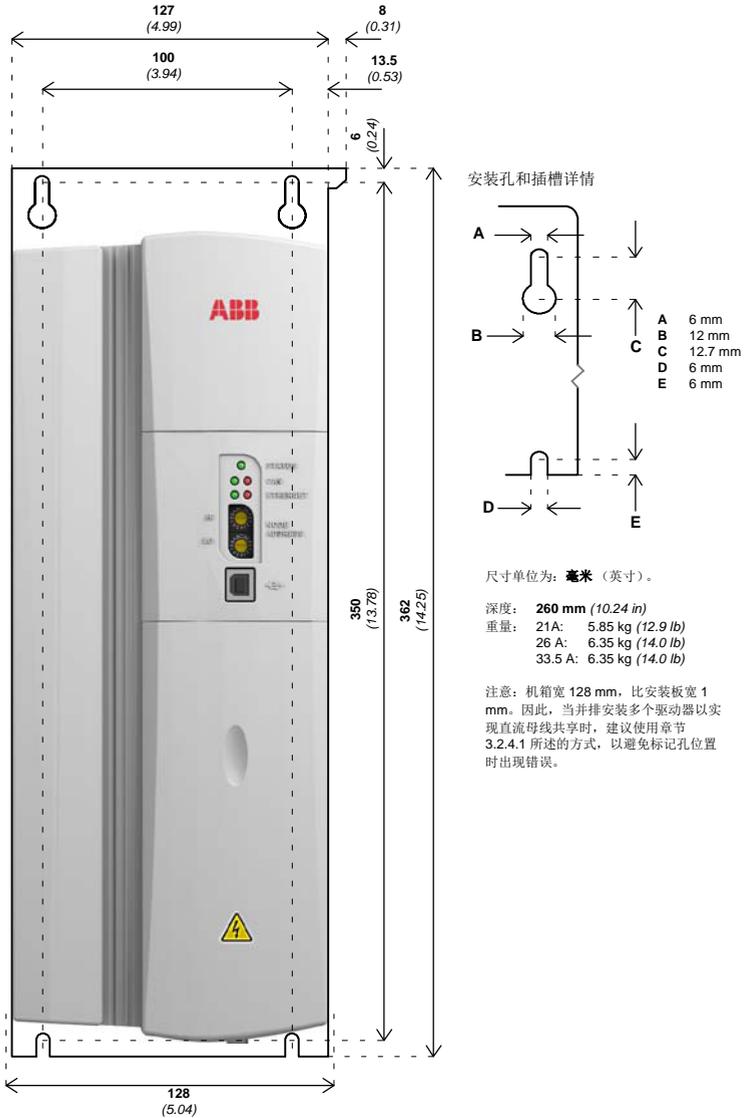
：安装尺寸和总体尺寸 - 21 A ~ 33.5 A 型
